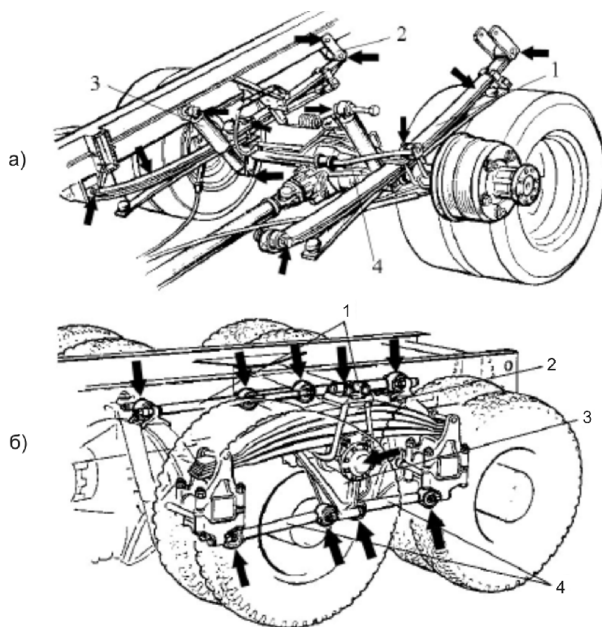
Зависимые рессорные подвески и основные места их контроля: а – подвеска одиночной оси (1 – рессора; 2 – серьга; 3 – амортизатор; 4 – стабилизатор); б – балансирующая тележка (1 – верхние реактивные тяги; 2 – рессора; 3 – балансирующее устройство; 4 – нижние реактивные тяги).
